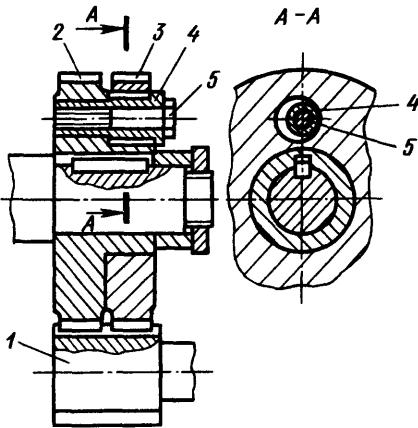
Беззазорная зубчатая передача с выборкой зазора разворотом эксцентриковой втулки
